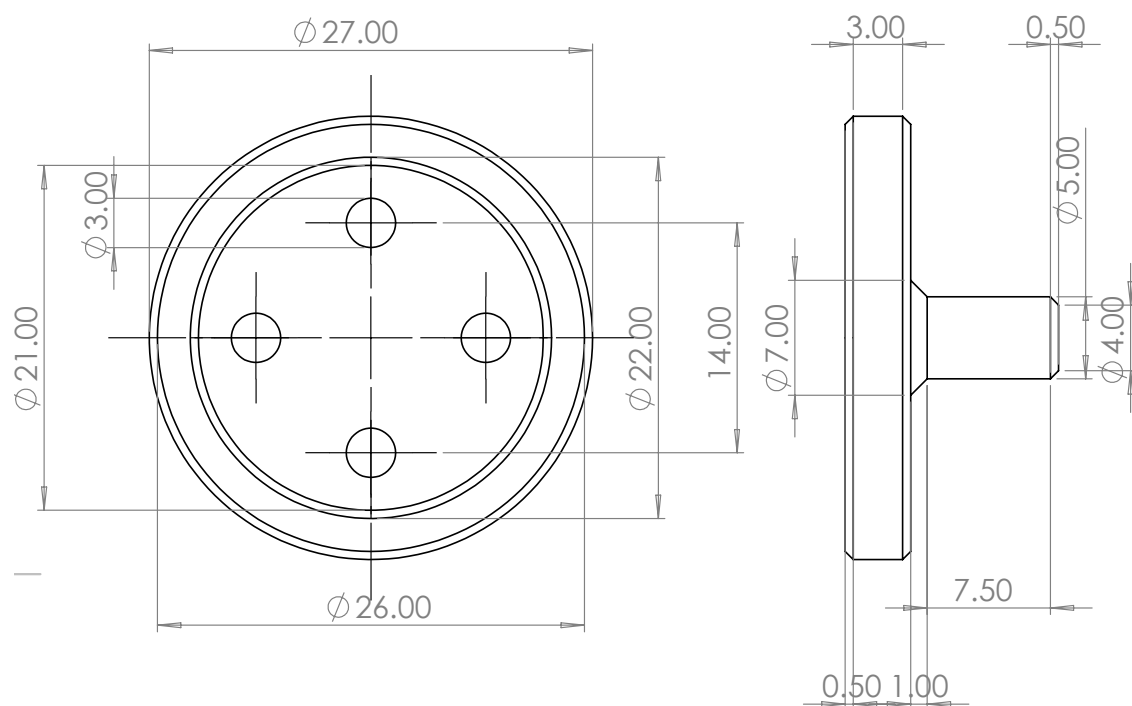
Mise en plan de la pièce palonnier avec dimensions
